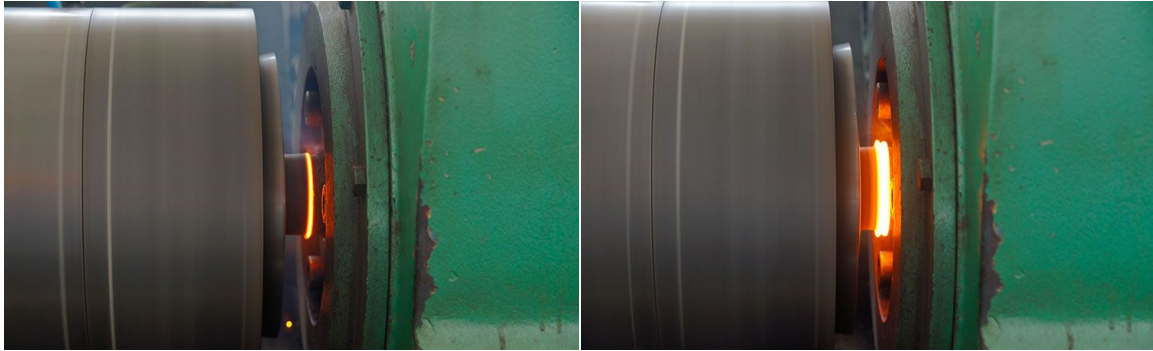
Principe de fonction de soudage par friction [20].
